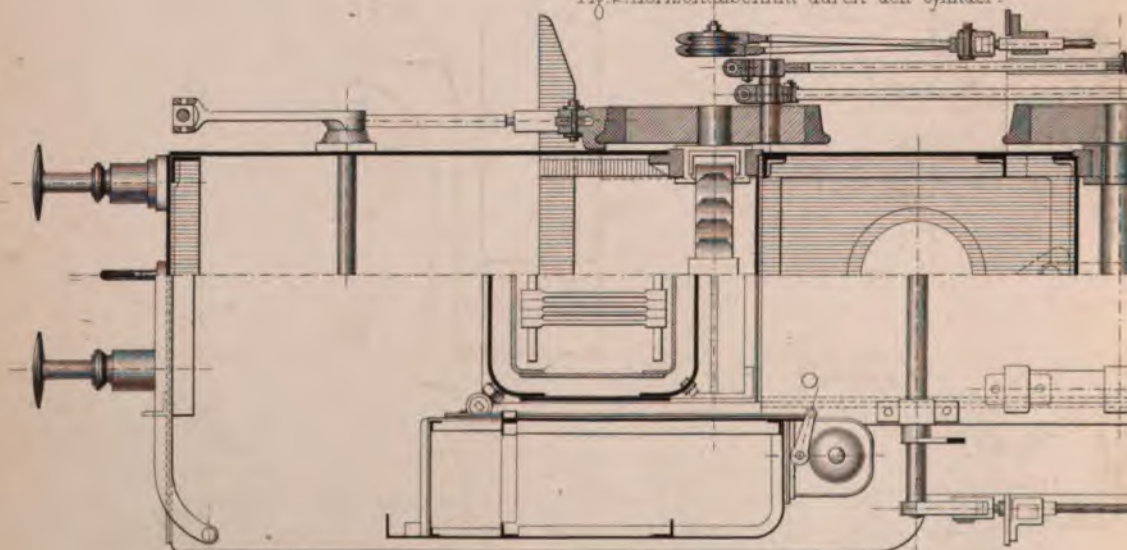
Horizontalschnitt über dem Wasserkasten.
